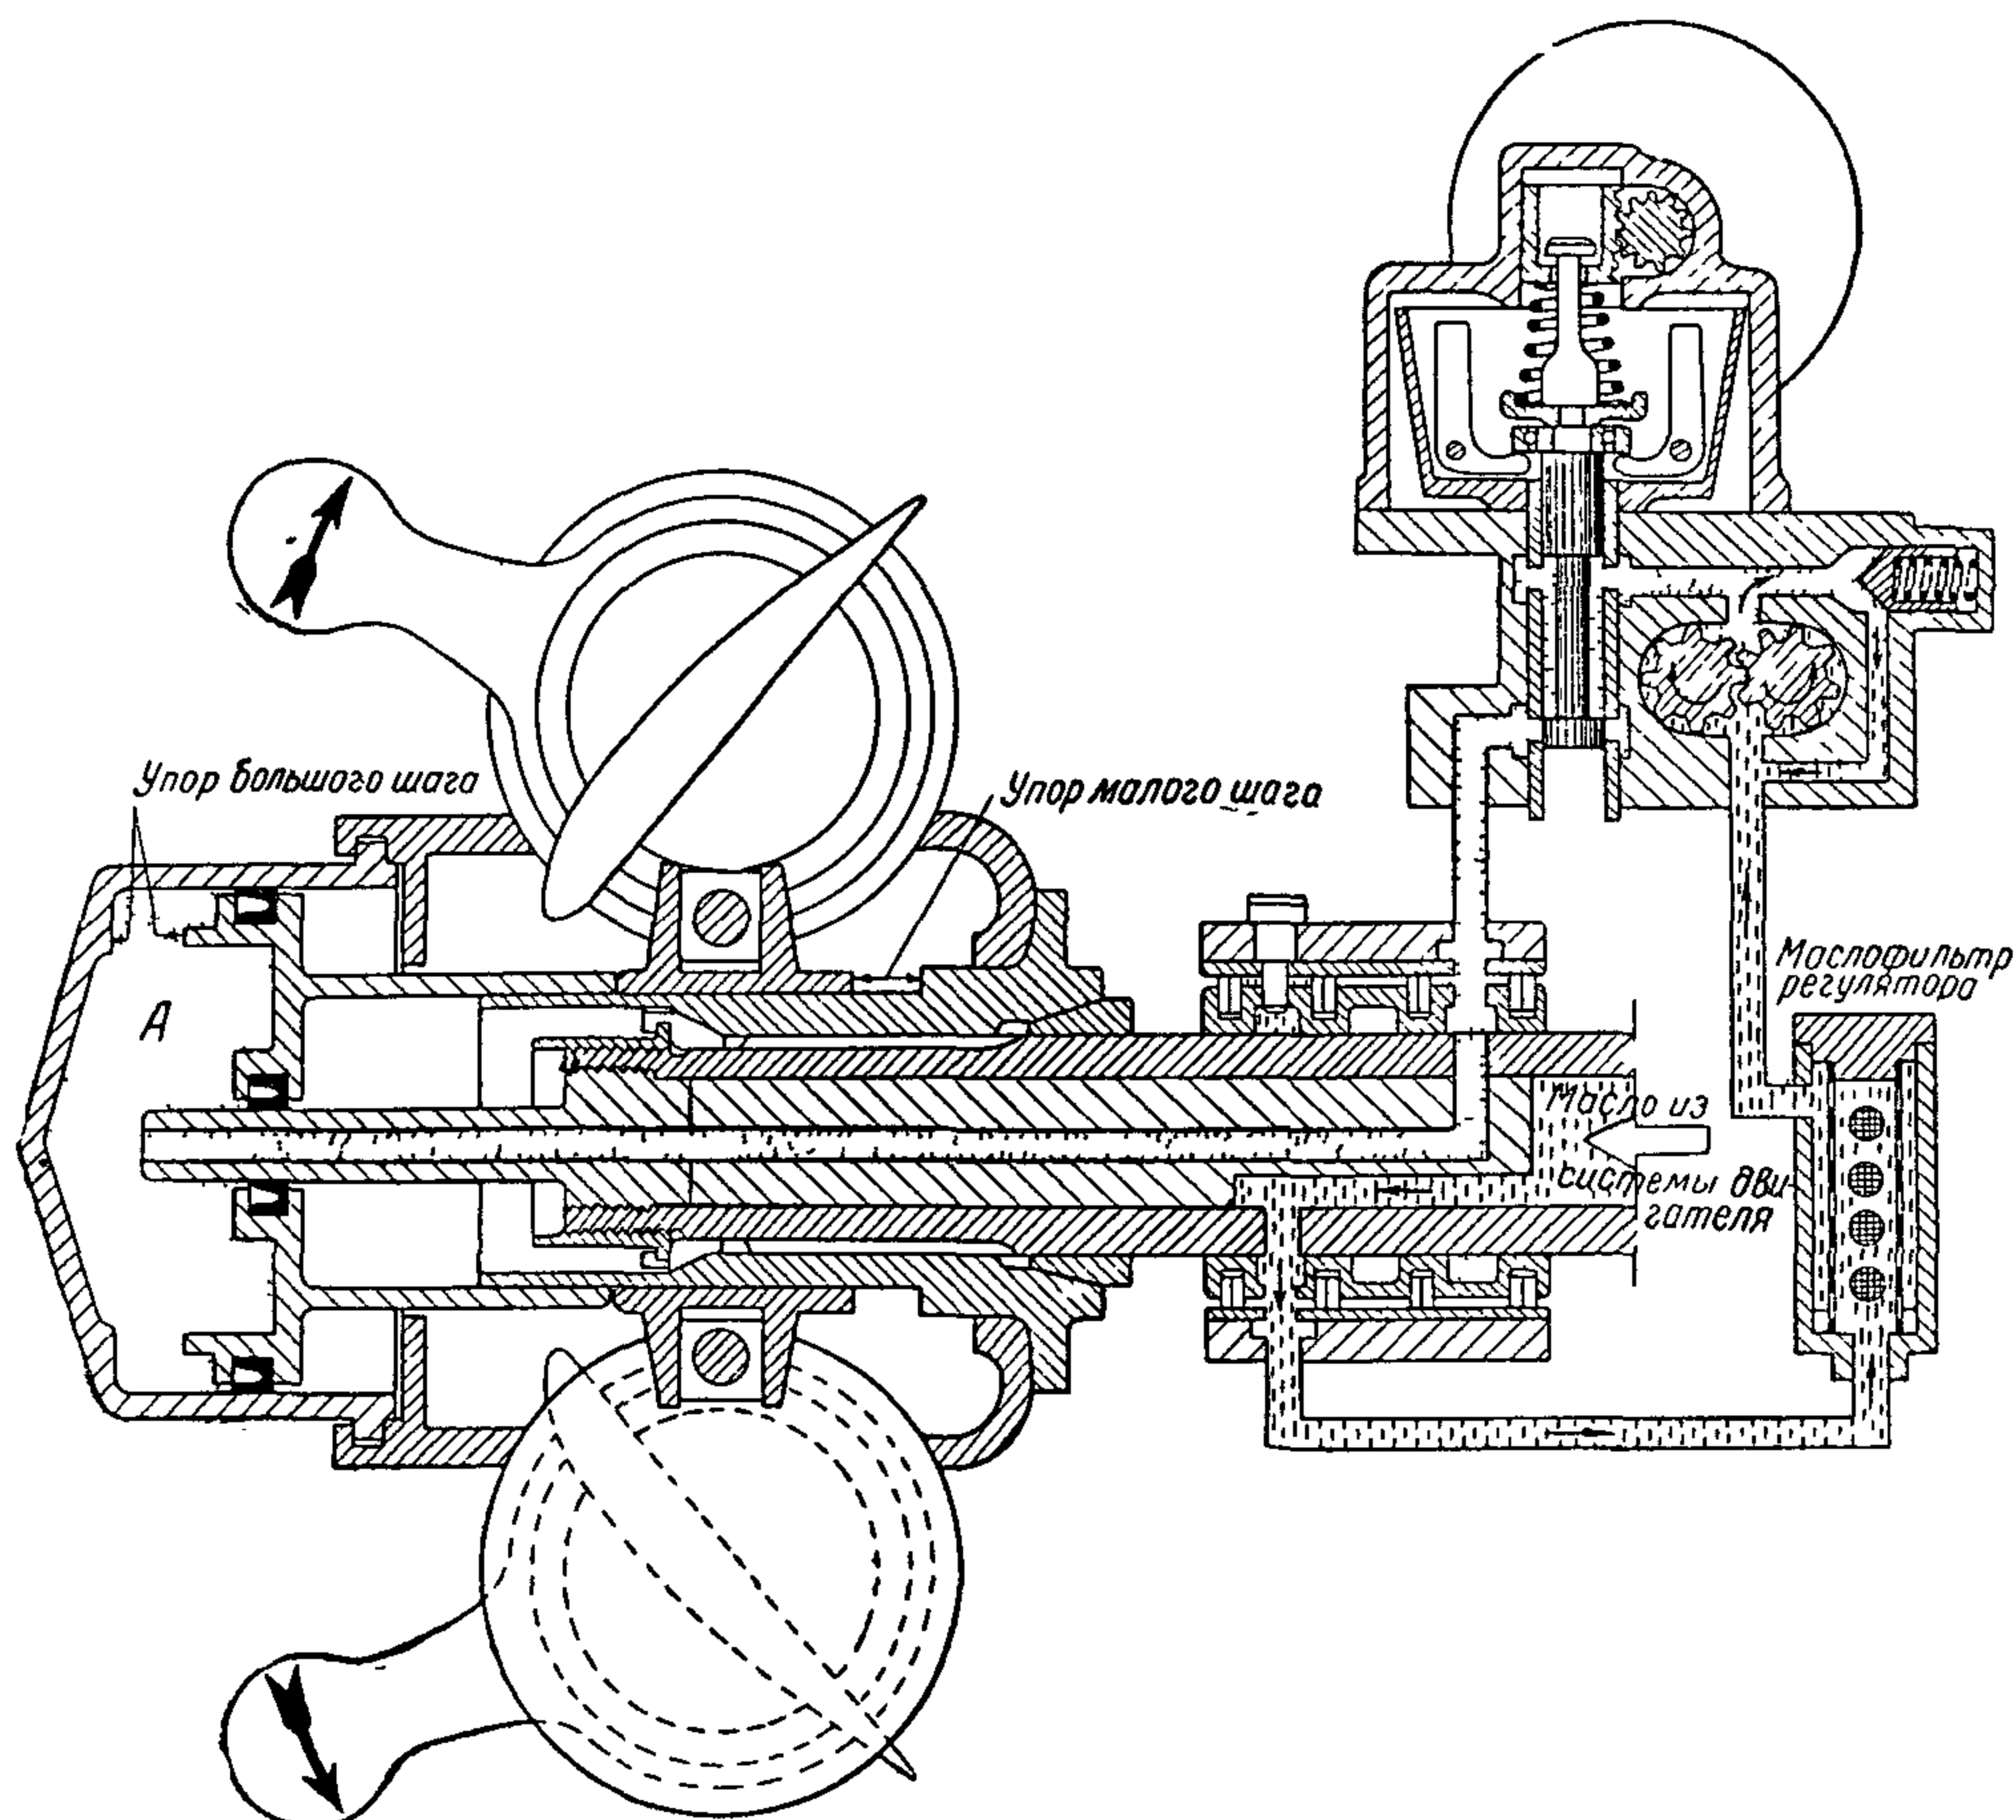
Схема работы механизма винта В-530 с регулятором постоянных оборотов Р-2 (положение деталей механизма винта и регулятора при равновесных оборотах)
